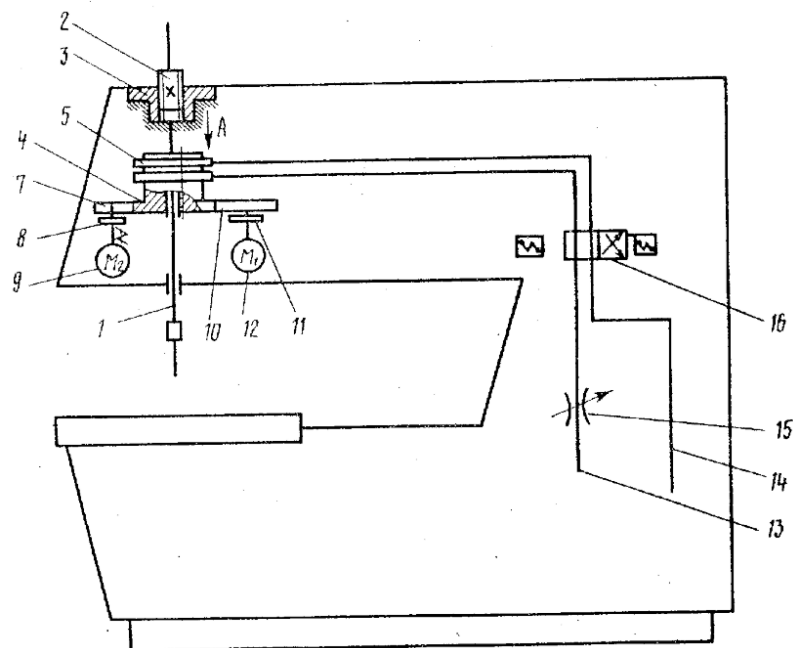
Резьбонарезной станок (авт. свид, 1061947А SU): 1 – шпиндель; 2 – винт; 3 – гайка; 4 – колесо привода; 5 – гидродвигатель; 6 – лопасть; 7 – зубчатое колесо; 8 – электромагнитная муфта; 9 – электродвигатель холостого хода; 10 – шестерня; 11 – электромагнитная муфта; 12 – электродвигатель рабочего хода; 13, 14 – каналы подвода; 15 – дроссель; 16 – распределитель
